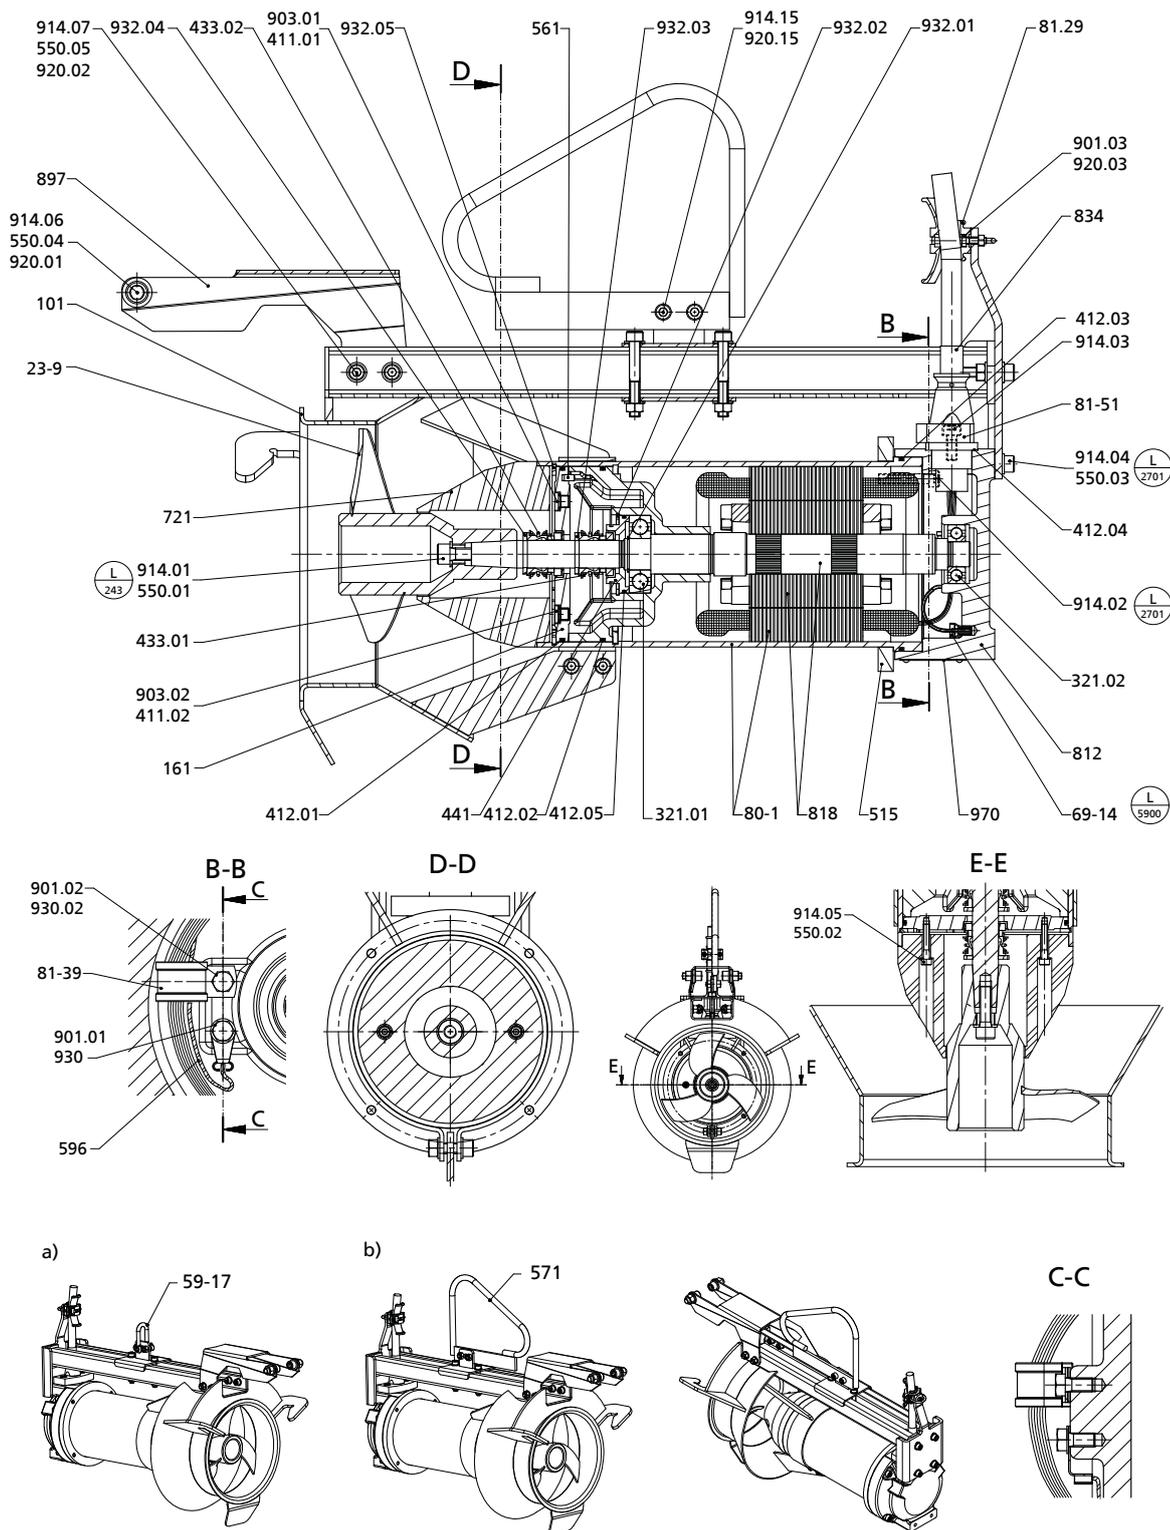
Чертеж общего вида: а) с серьгой б) со скобой (дополнительно)
